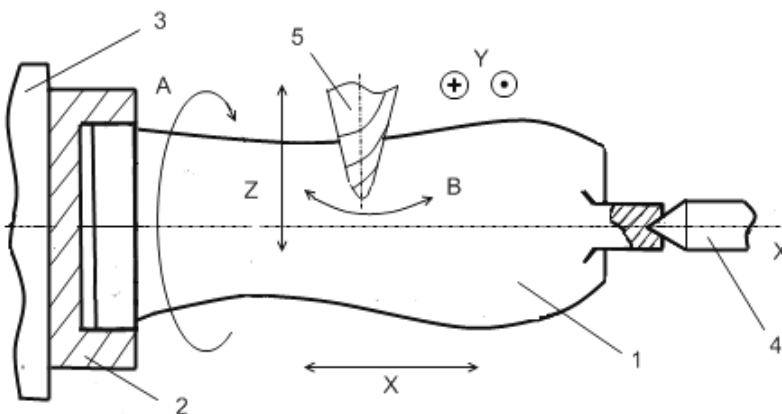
Схема взаимных перемещений инструмента и заготовки при фрезеровании проточной части лопатки, где: 1 – заготовка; 2 – приспособление; 3 – планшайба передней бабки; 4 – центр задней бабки; 5 – инструмент
